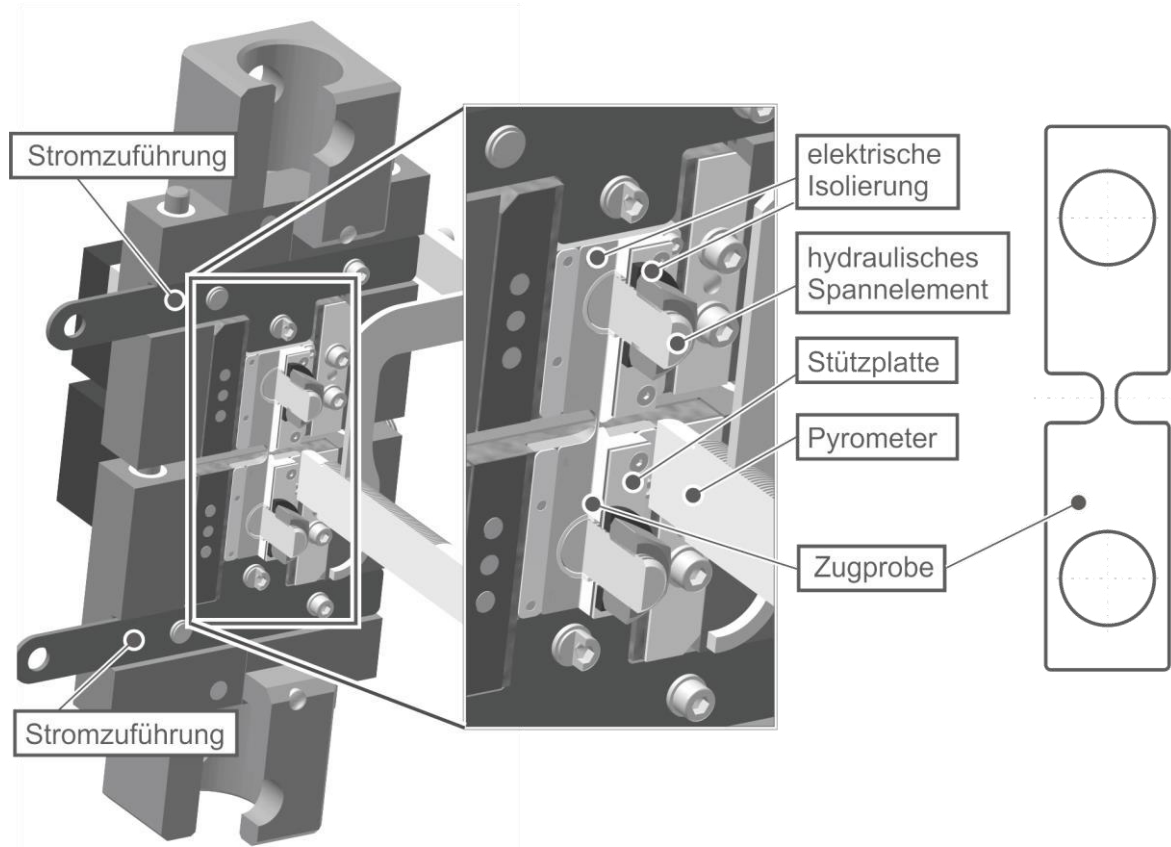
Zug- und Druckwerkzeug für die Werkstoffcharakterisierung bei erhöhten Temperaturen
